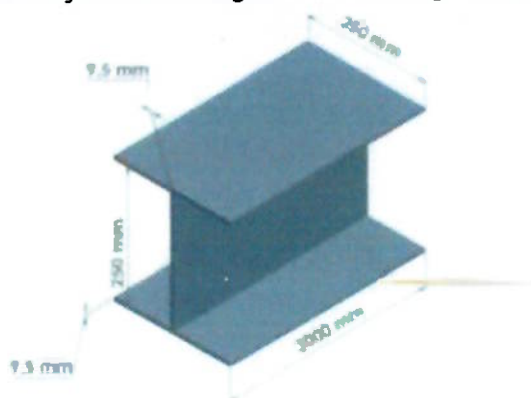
Segunda execução de soldagem concluindo o perfil "I".
